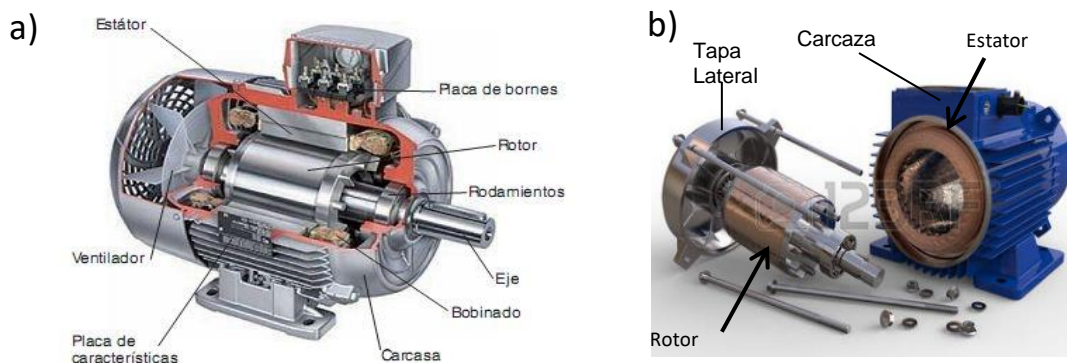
Motor eléctrico, a) partes principales, y b) Motor desarmado mostrando el rotor y estator
